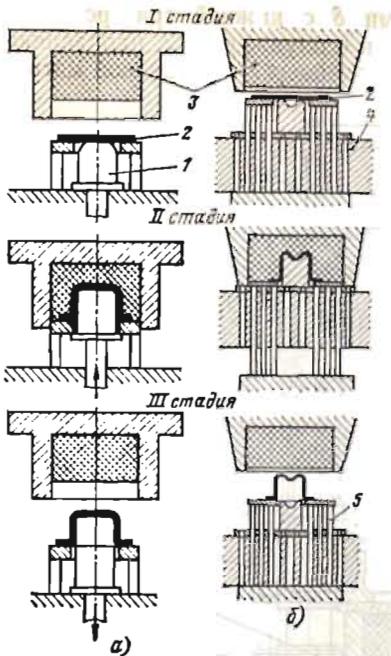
Схема работы прессов: а) ПШВР-1; б) ПШВР-3; 1 — пуансон; 2 — заготовка; 3 — резиновая подушка; 4 — стол пресса; 5 — опорная колонна
